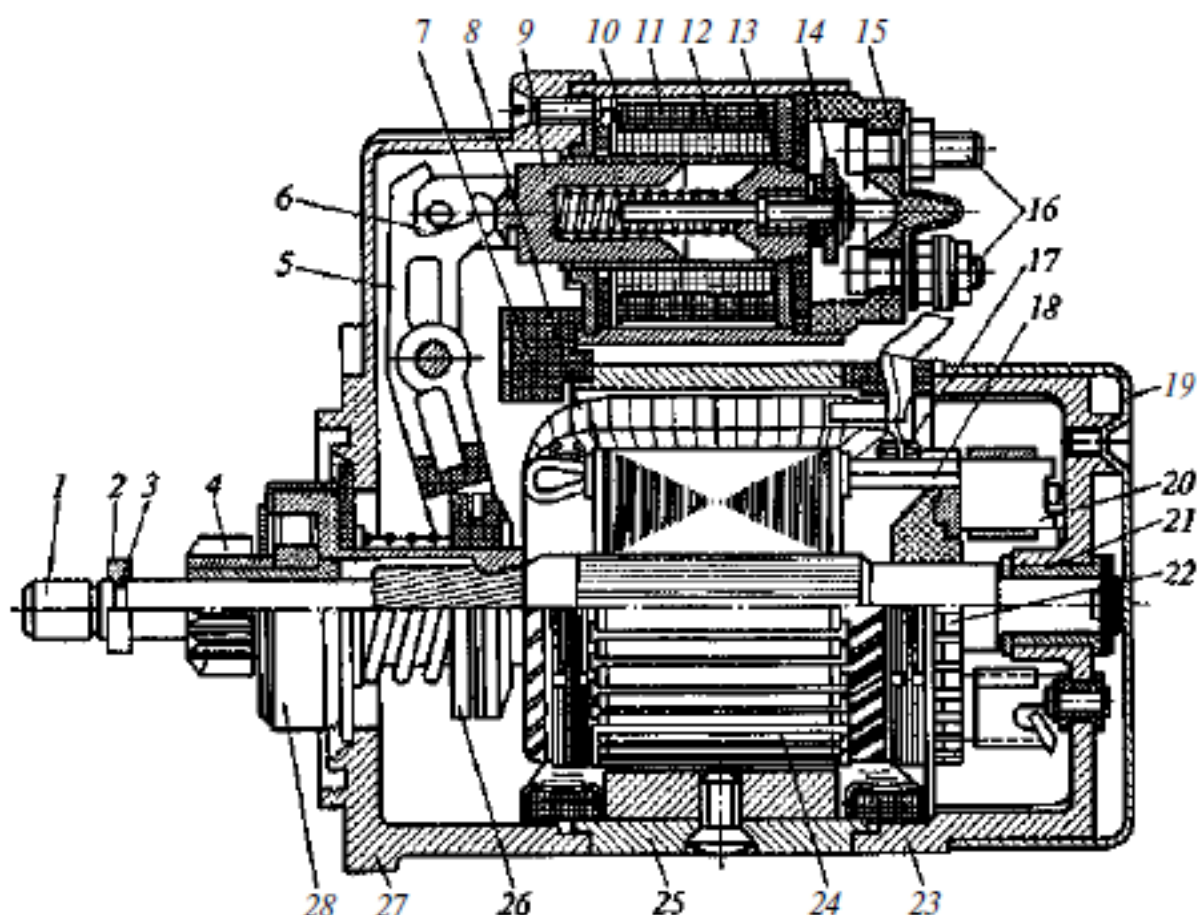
Электростартер с торцевым расположением щеток: 1 – вал якоря; 2 и 3 – соответственно замковое и упорное кольца; 4 – шестерня; 5 – обмотка реле; 6 – тяга реле; 7 – заглушка; 8 – обмотка возбуждения; 9 – якорь тягового реле; 10 и 15 – корпус и крышка тягового реле; 11 и 12 – удерживающая и втягивающая обмотки; 13 – сердечник втягивающего реле; 14 – подвижный контакт; 16 – контактные болты; 17 – бандаж обмотки якоря; 18 – обмотка якоря; 19 – защитный кожух; 20 – щетка; 21 – подшипник скольжения; 22 – торцевой коллектор; 23 – коллекторная крышка; 24 – якорь стартера; 25 – корпус; 26 – поводковая муфта; 27 – передняя крышка; 28 – роликовая муфта свободного хода
